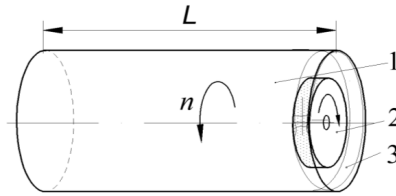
Схема обробки внутрішньої поверхні циліндра:
